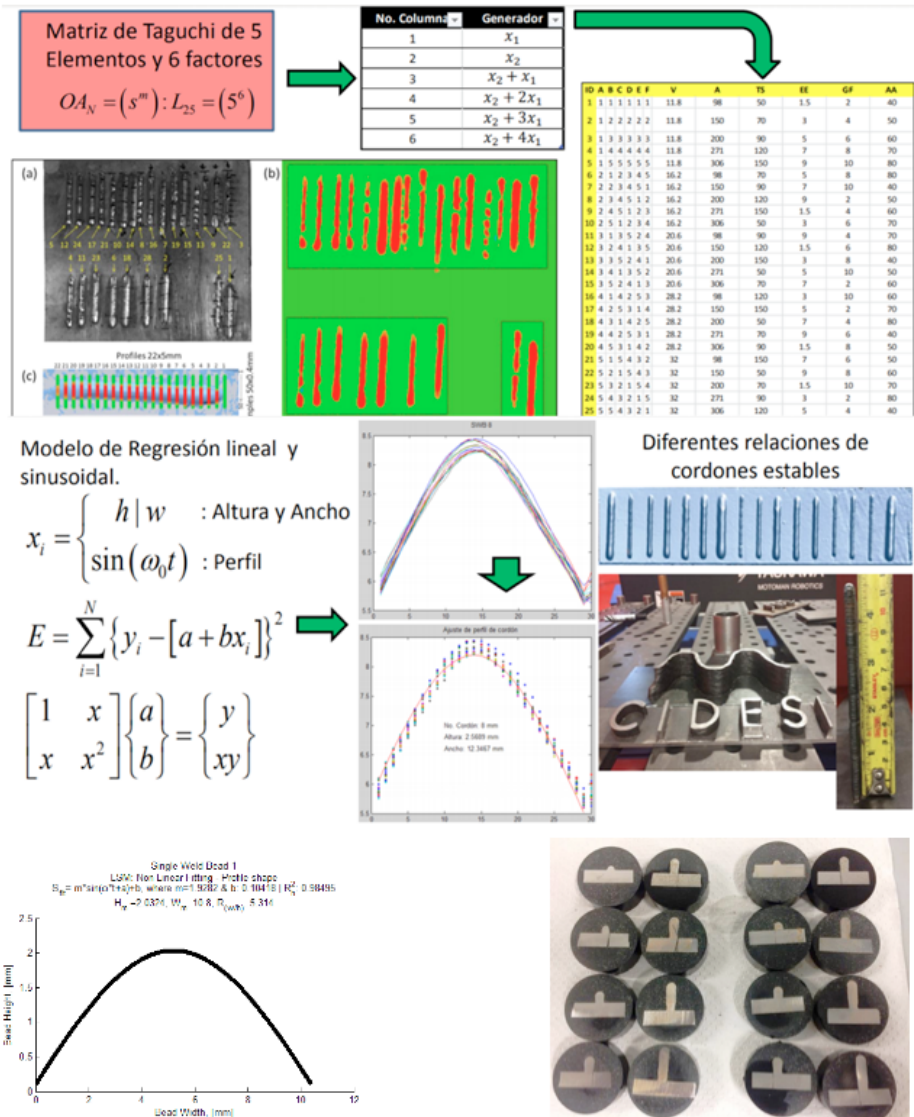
Proceso de optimización mediante Taguchi para soldadura robotizada CMT con alambre ER70S-6 [24]
